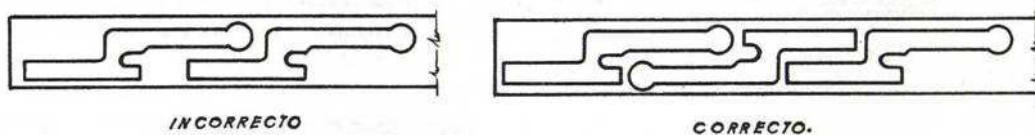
Distribuciones de piezas sobre la plancha metálica.
